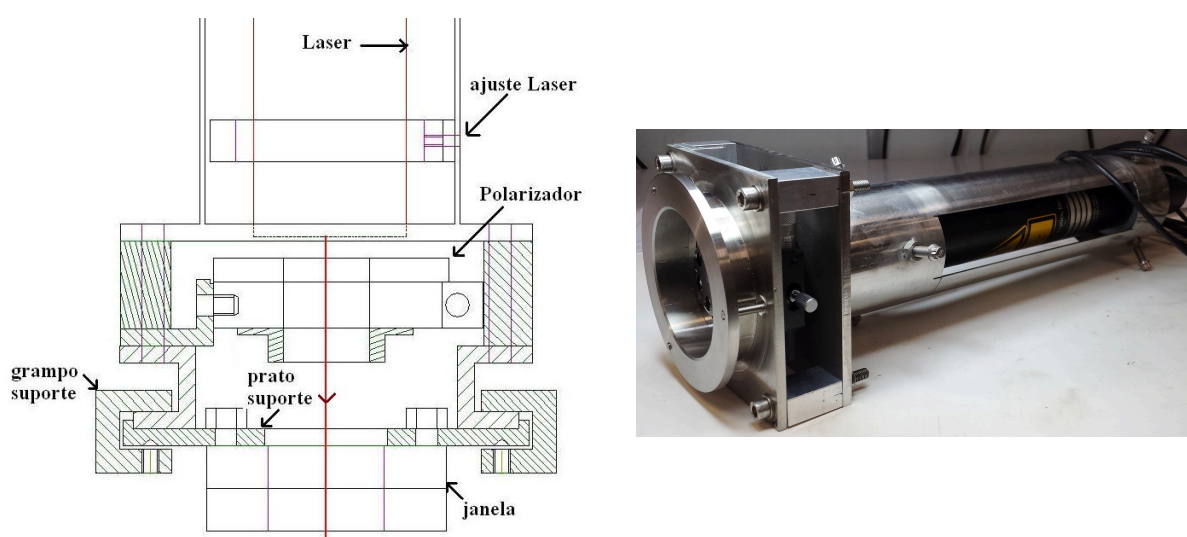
Desenho técnico do suporte para o laser centrado na janela e foto do suporte montado.
